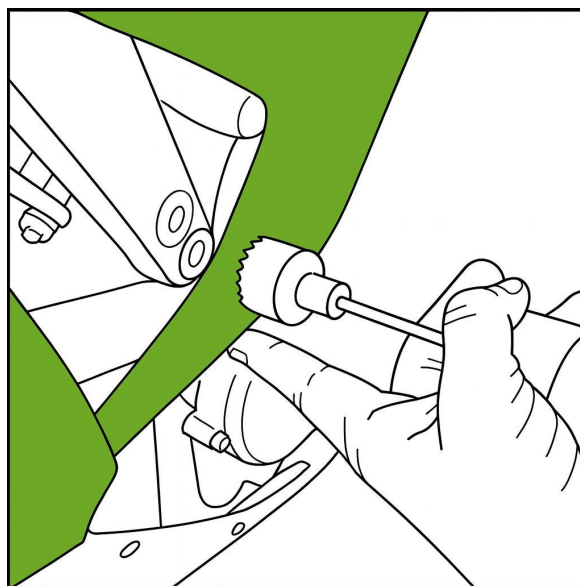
Доработка пластика сверлением коронкой (на примере левой стороны)
